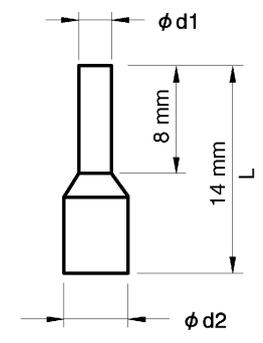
Dimensions des bornes droites sans soudures
